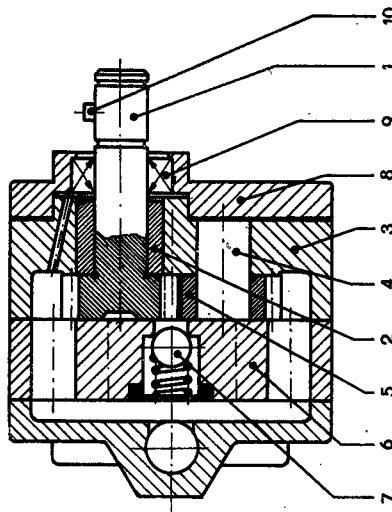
Рис. I Шестеренчатый насос номинальная величина I,6 или 2,5
